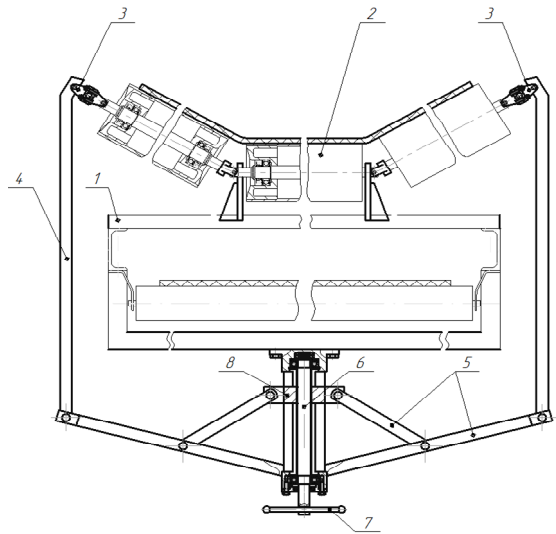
Поперечний переріз стрічкового конвеєра з механізмом регулювання форми стрічки
